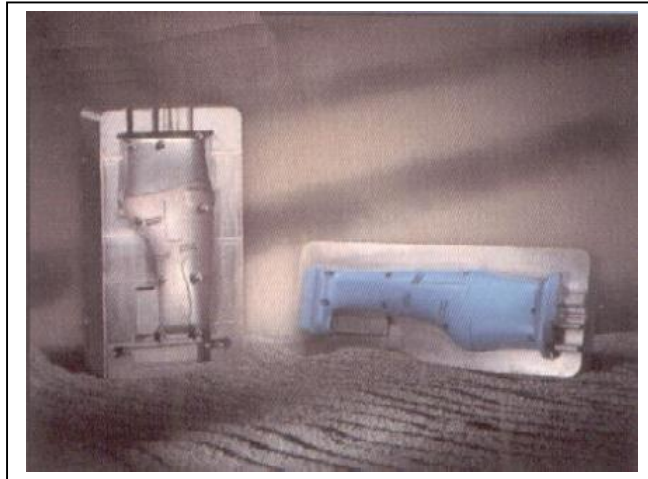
Pieza fabricada en Rapid Steel 2.0
